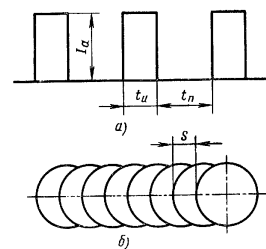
Схемы процесса сварки импульсной дугой:
